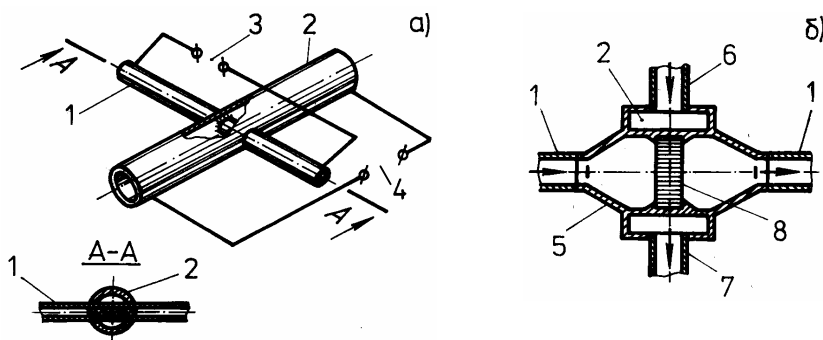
Запірний пристрій для: а – розплавлених металів [13]; б – рідкометалевих носіїв [14]:
